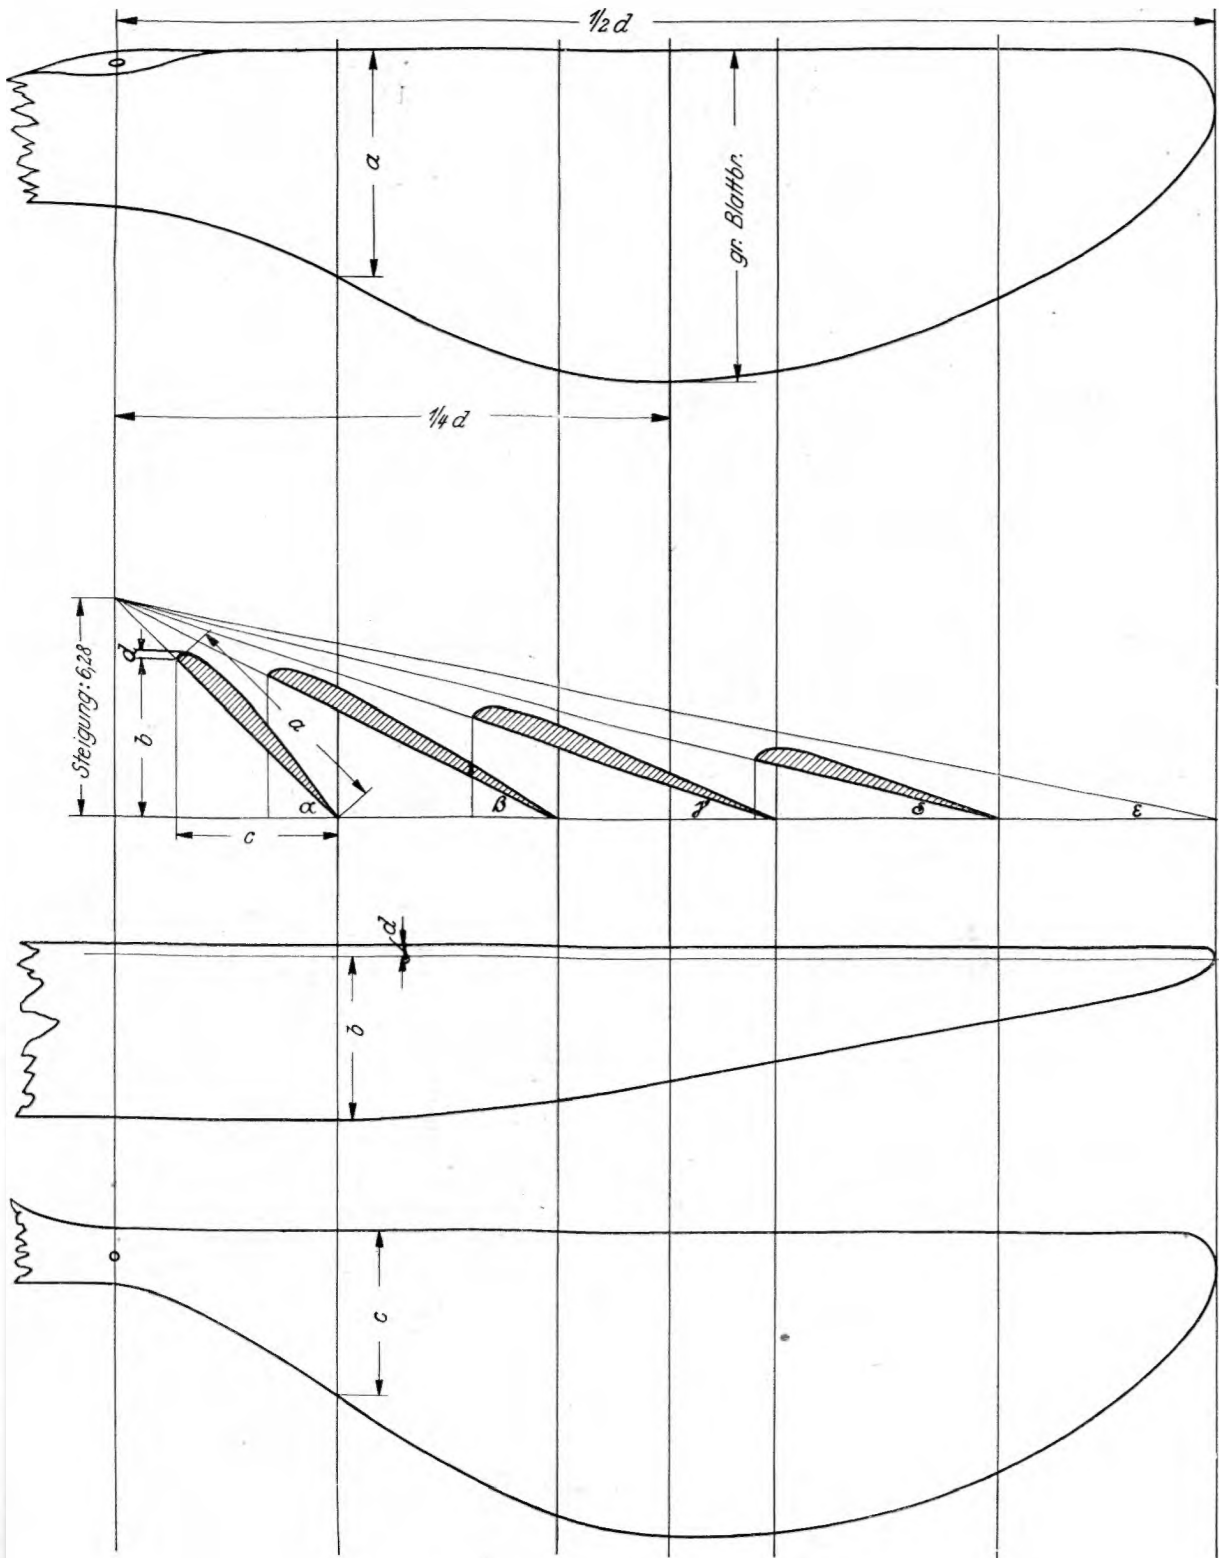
Die Bauzeichnung der Luftschraube (verkleinert).
